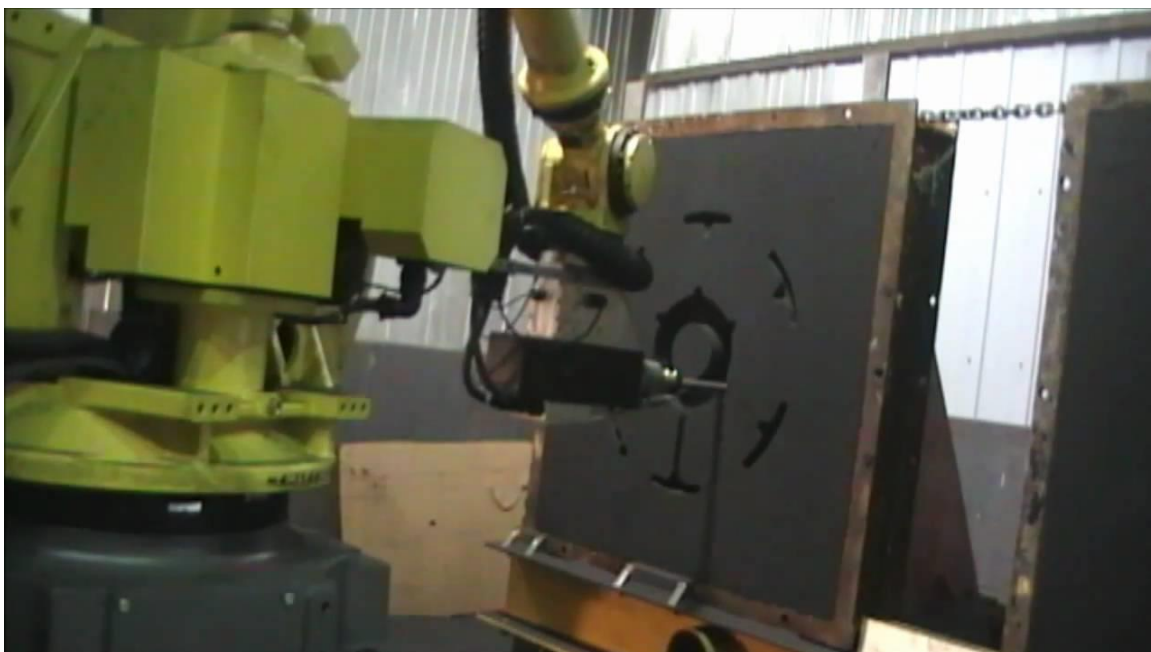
Forma hlavy motoru vyrobená metodou DSPC [23]
